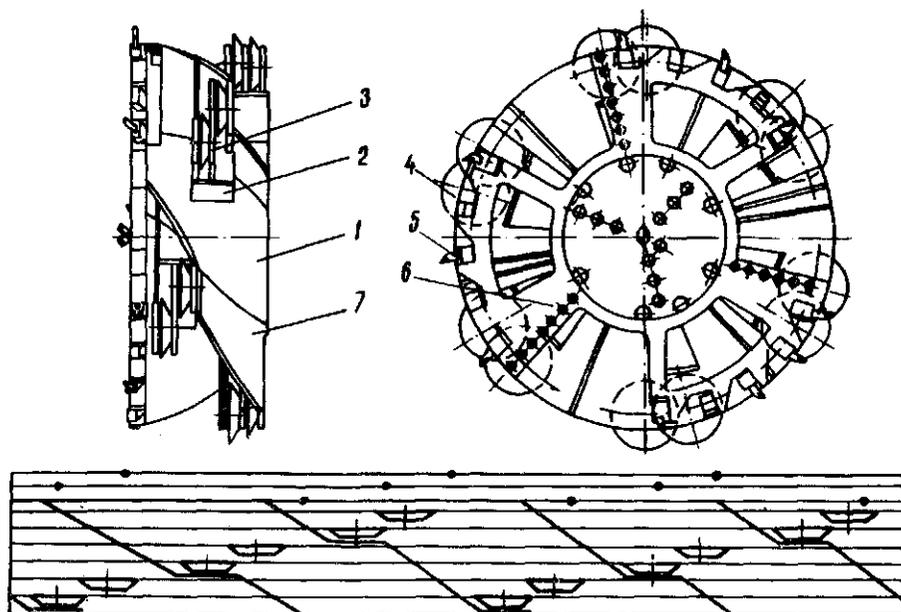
Общий вид шнека с дисковыми шарошками и схема набора инструмента
